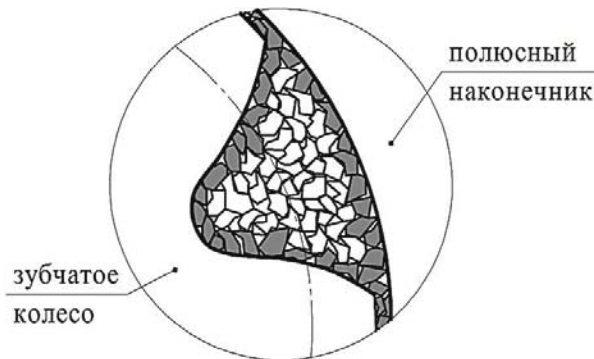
Схема расположения уплотненного абразивного бруска во впадине зубчатого колеса [12]
